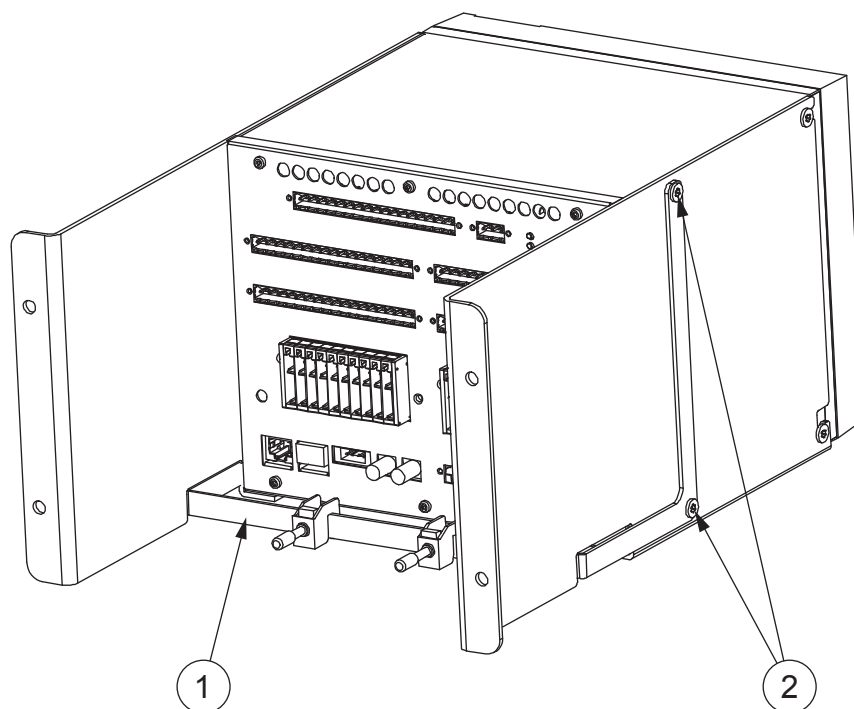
Montaje del bastidor de pantallas de cables opcionales
